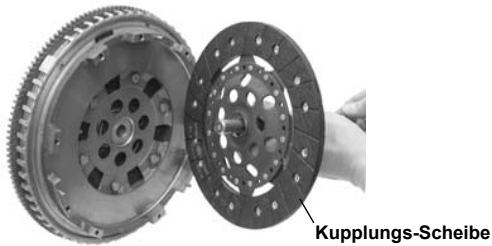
Kupplungs-Zentrierwerkzeug spannen.
